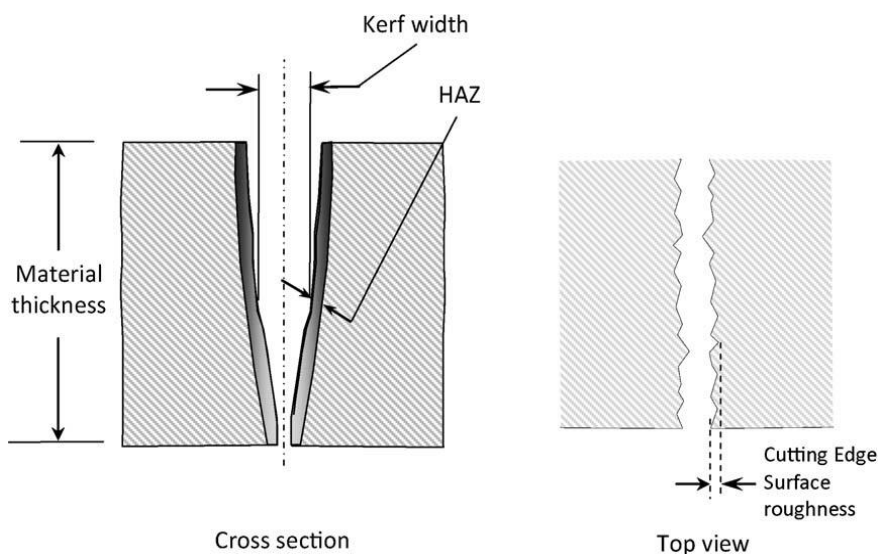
Parameter pemotongan pada *Laser Cutting
